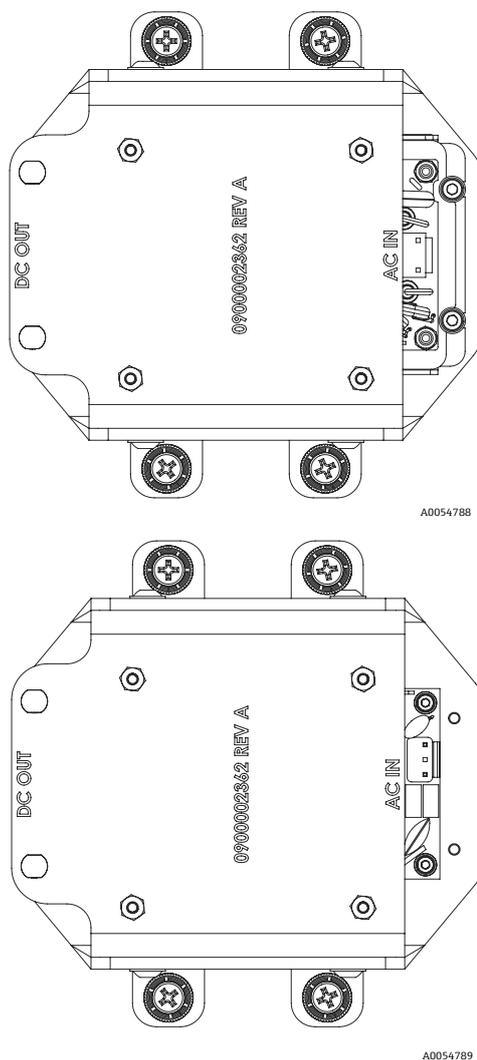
Монтажное положение блока питания: TDK (сверху) и Sincon (снизу)
